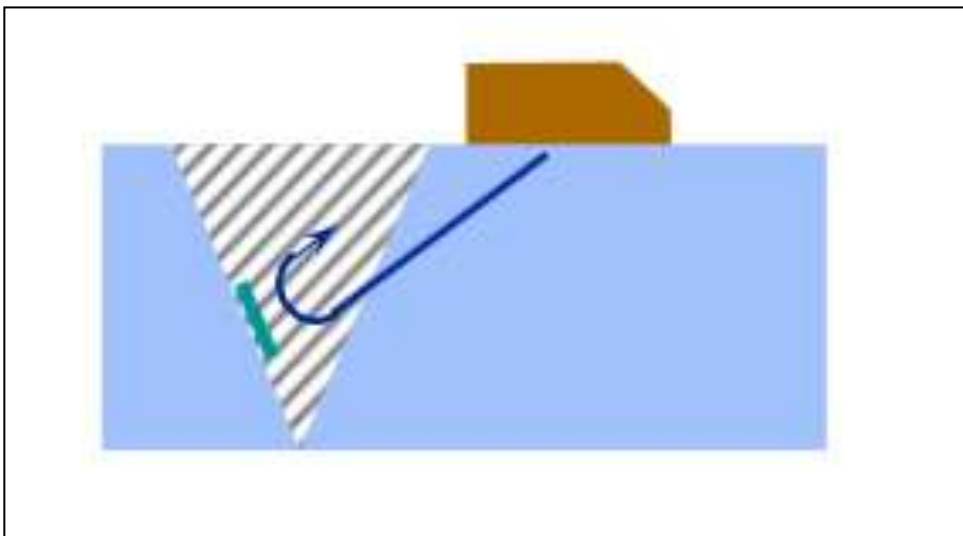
Position de la sonde par rapport au joint de soudure [30].
